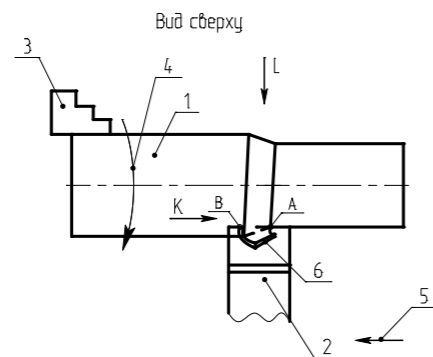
Схема обработки деталей безвершинным проходным токарным резцом
